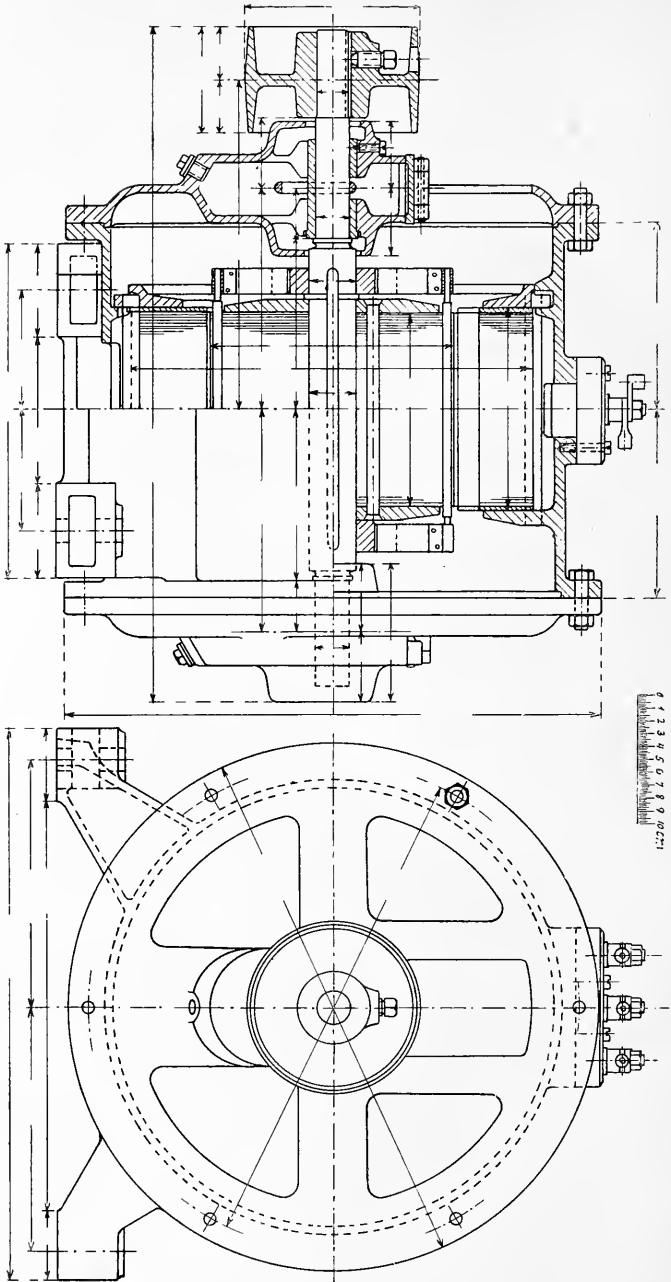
Fig. II. Gesamtzeichnung. (Drehstrommotor von Kolben & Co., Prag).
